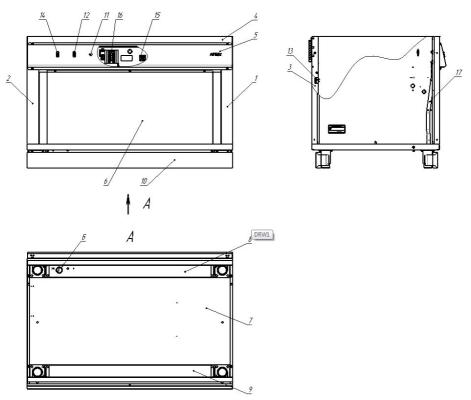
1, 2- стенка боковая; 3- стенка задняя; 4- кожух; 5- панель управления; 6- передняя панель; 7- днище; 8, 9- швеллер; 10- плинтус; 11- лампа; 12- выключатель; 13- клеммный блок; 14- выключатель; 15- клеммный блок; 16- клеммный блок; 17- трубка гибкая.
